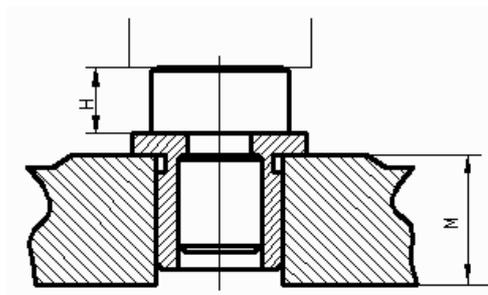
Установка опор постоянных в корпусе приспособления.
